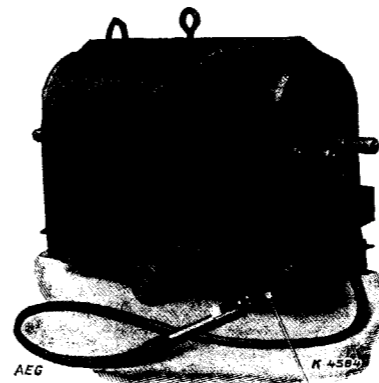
^a—Transformador especial para soldadura por arco con corriente alterna.
